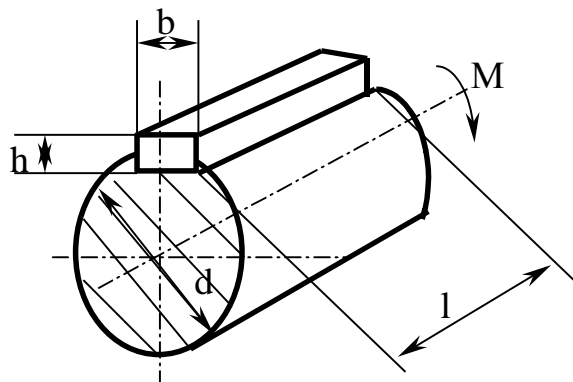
Розрахункова схема шпонкового з'єднання.
